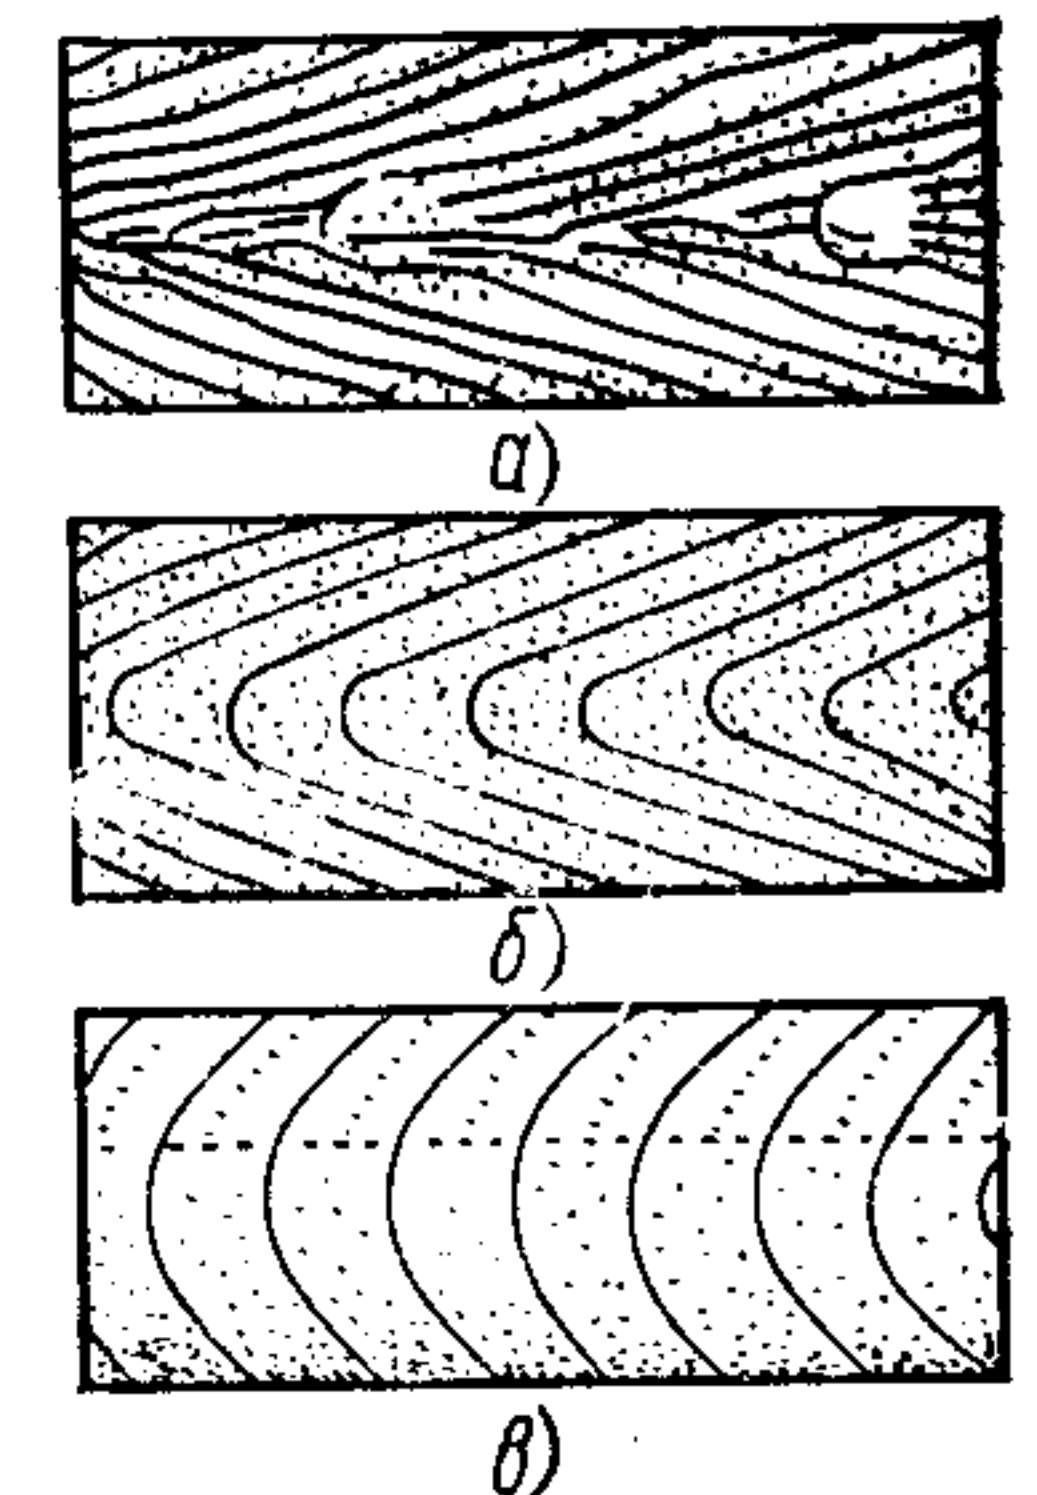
Влияние опережения на внешний вид наплавленного валика:
